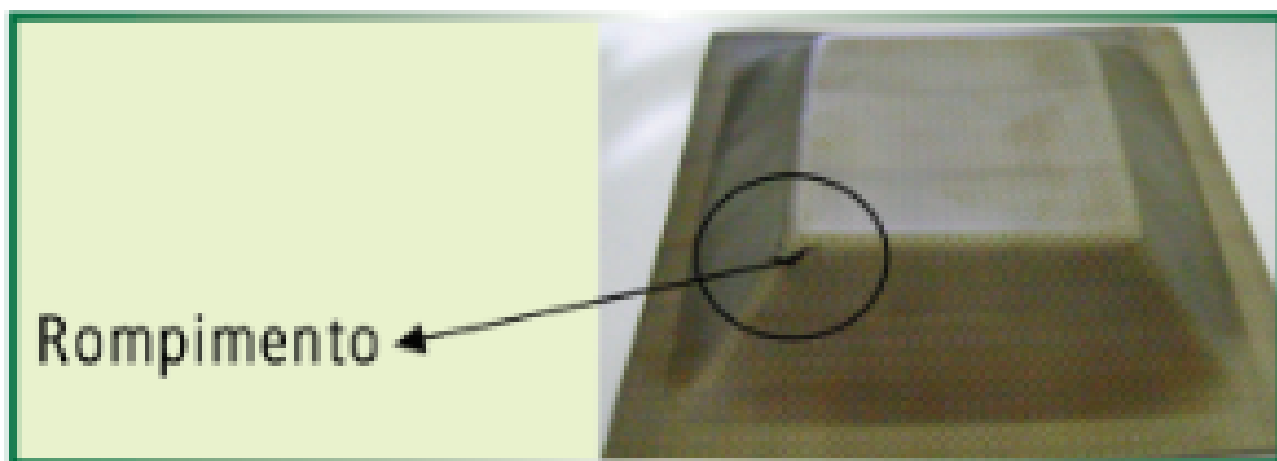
Teste de estampagem SPIF com 48° de ângulo de parede
